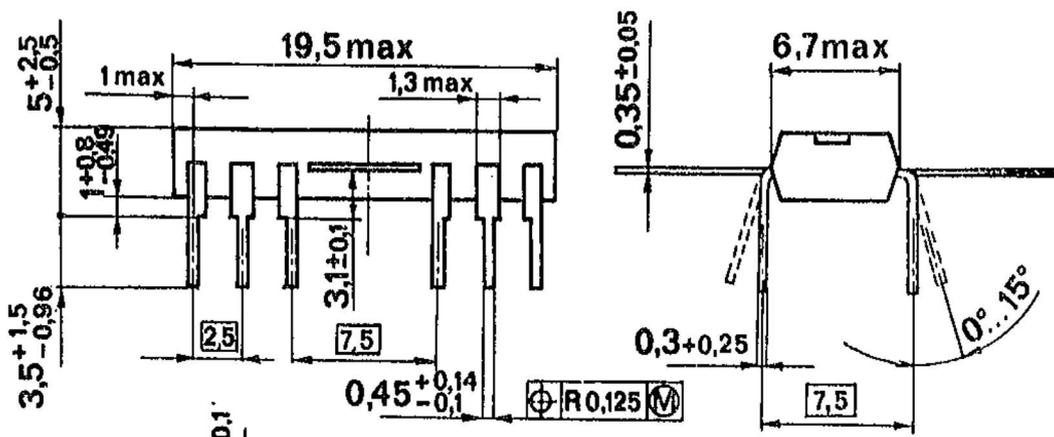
(DIP-12, Plast mit Kühlkörperanschluss)
